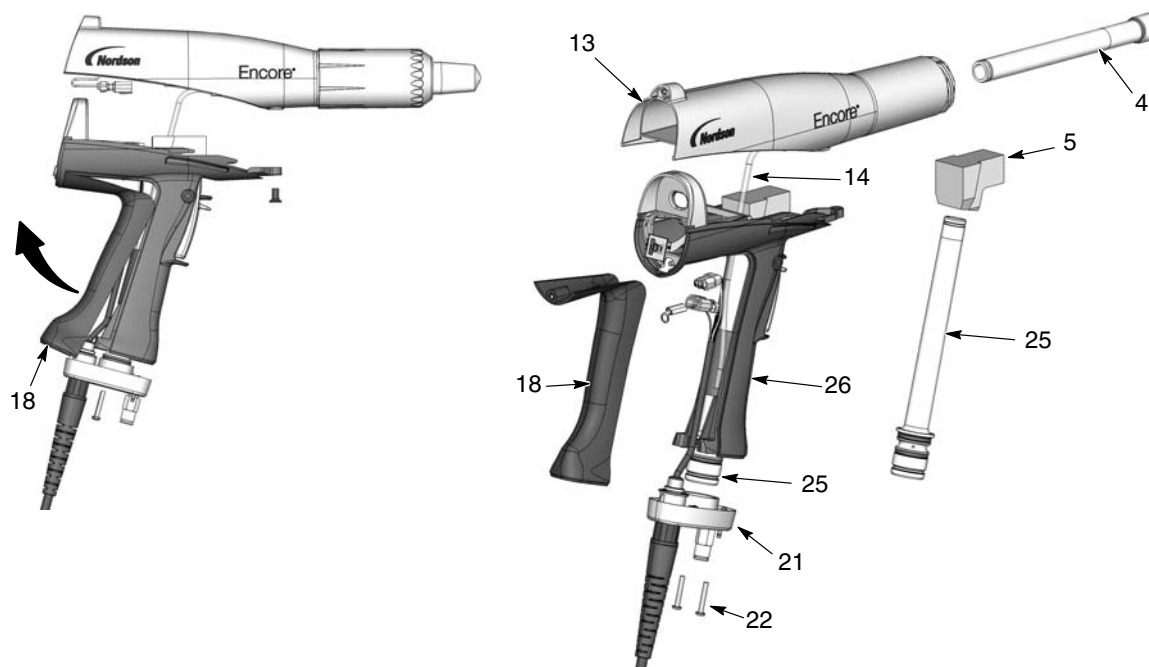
Demontáž napájecího zdroje z tělesa pistole
